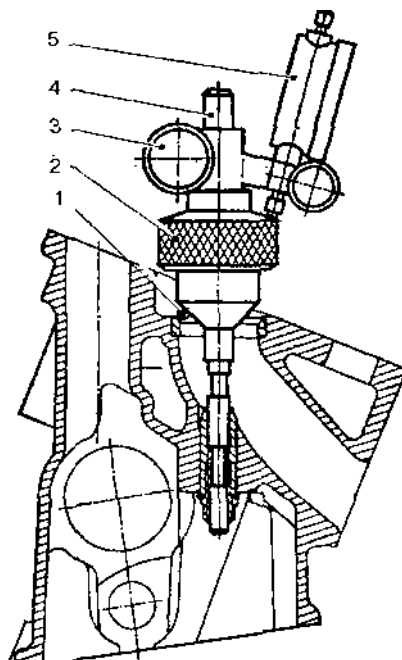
Приспособление для проверки concentricity фаски седла клапана и оси направляющей втулки:
